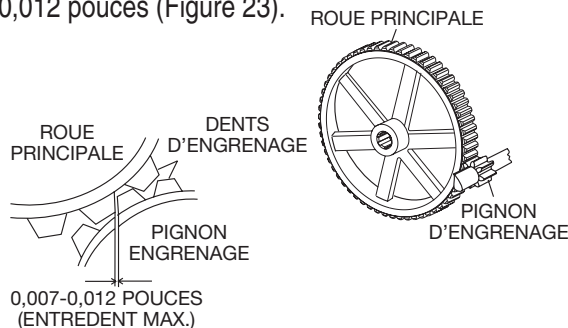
Pignon d'engrenage et engrenage principal (réaction)
